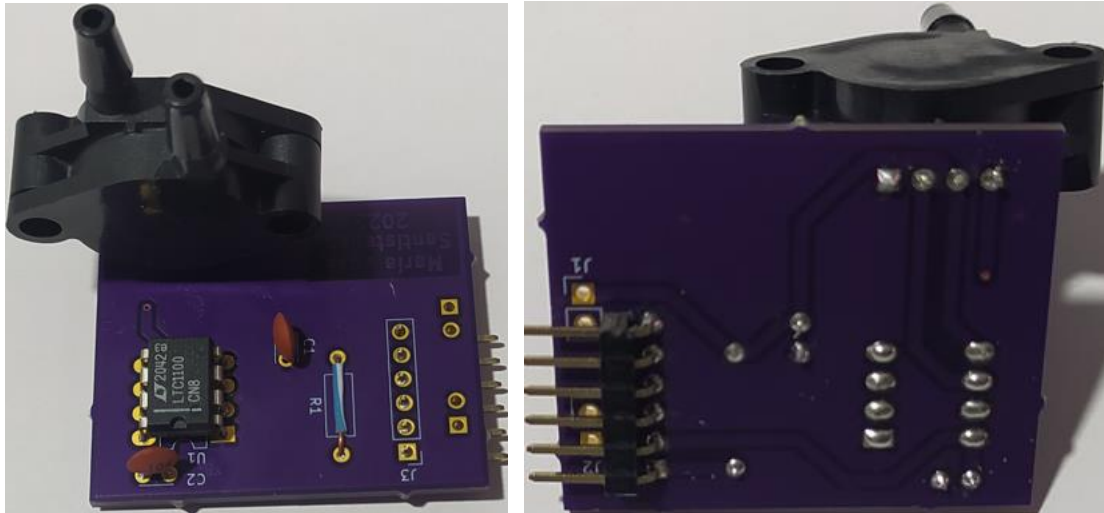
Placa de Circuito impreso con elementos soldados (elaboración propia)
